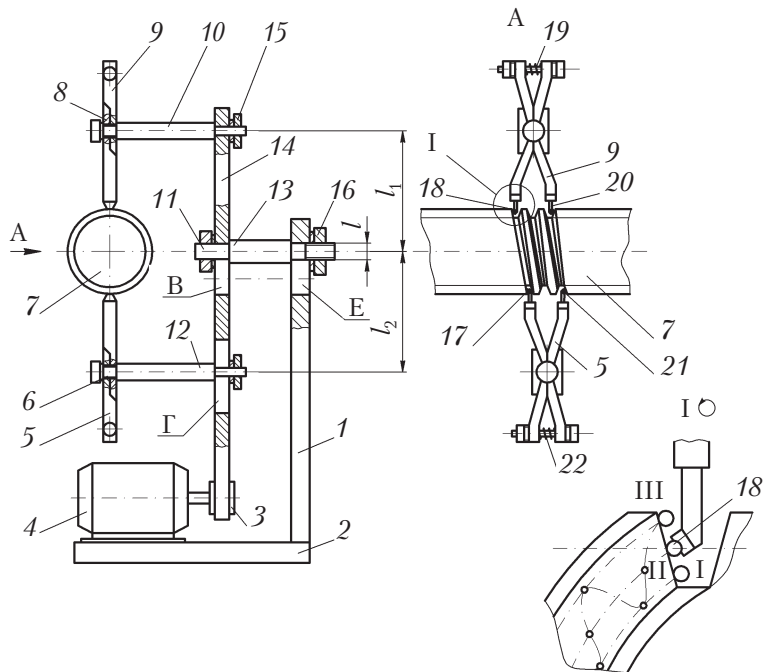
Устройство для вибронакатывания поверхностей винтов
